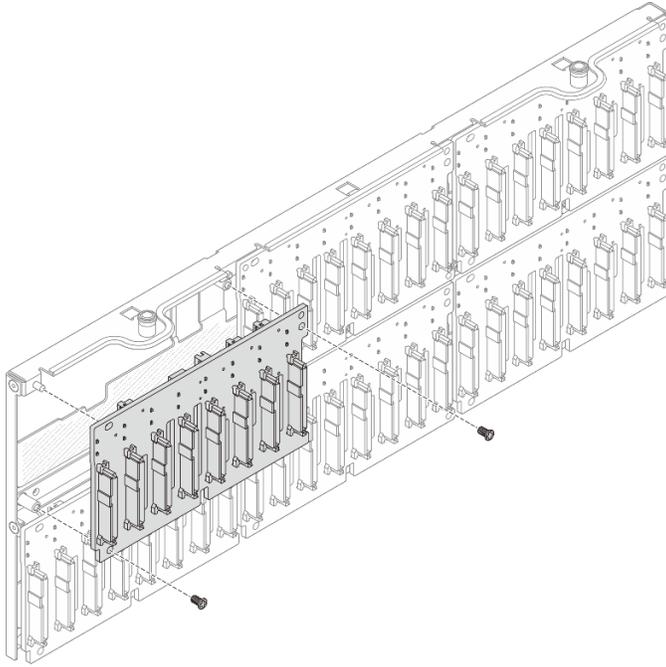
Installation du fond de panier sur le support (châssis doté d'une baie 2,5 pouces)
